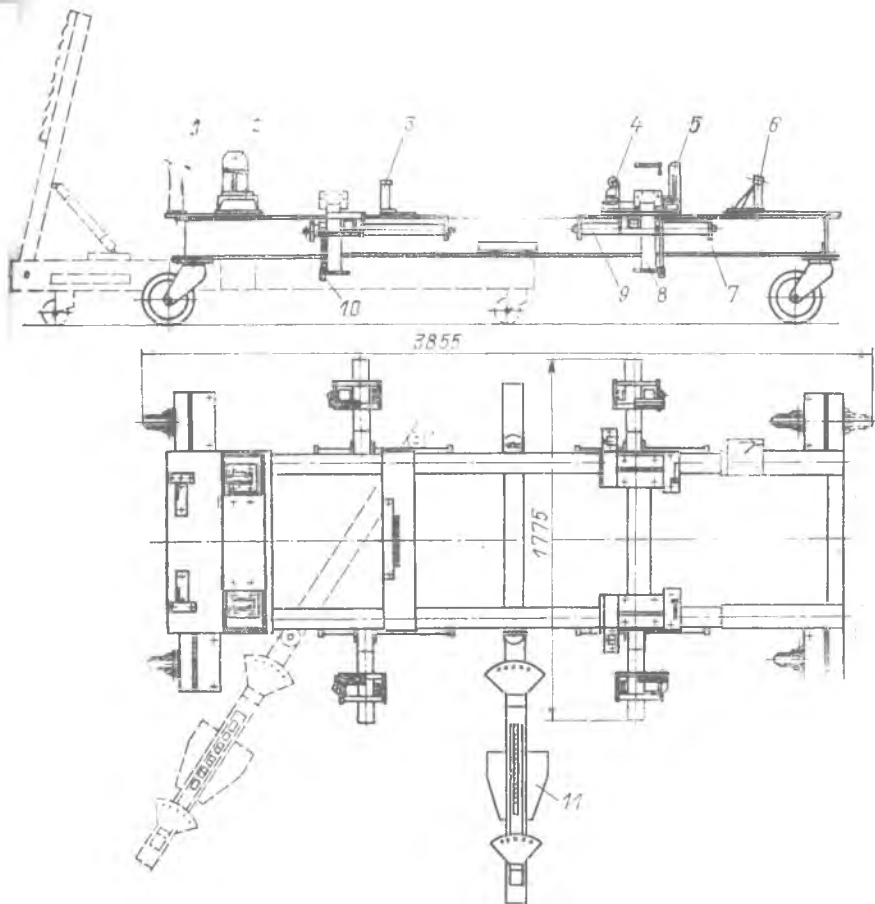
Установка БС-123.000 для правки и контроля кузовов автомобилей «Жигули»
